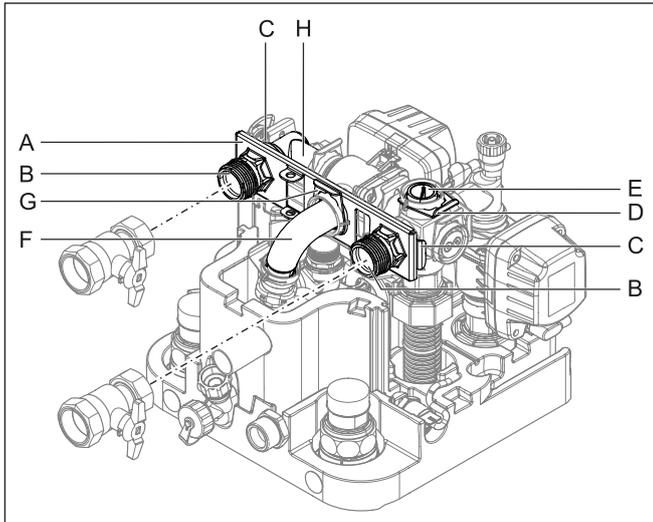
Anschlüsse Heizungs- vor- und -rücklauf nach hinten ausgerichtet
